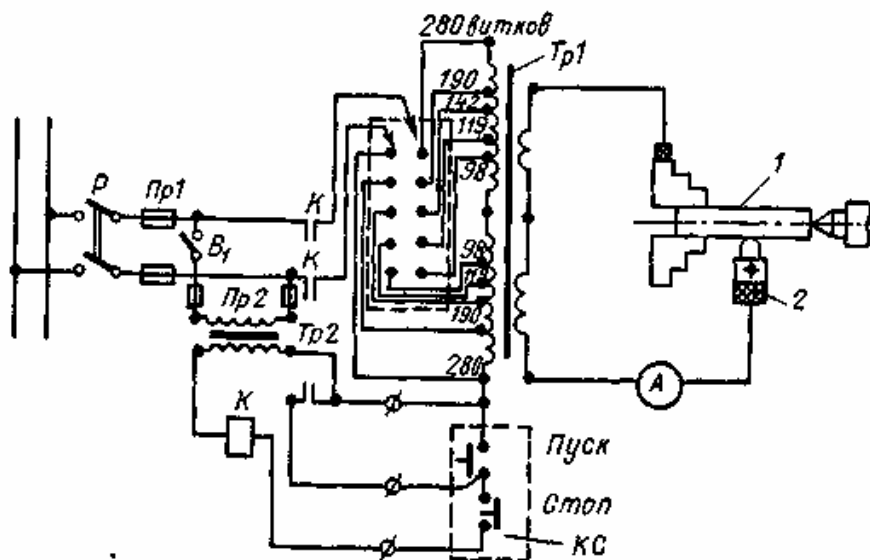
Схема установки для электромеханической обработки: 1 – заготовка; 2 – инструмент; А – амперметр; КС – кнопочная станция; К – контакты и контактор; Tr1 и Tr2 – трансформаторы; Pr1 и Pr2 – предохранители; B<sub>1</sub> – выключатель; P – рубильник
